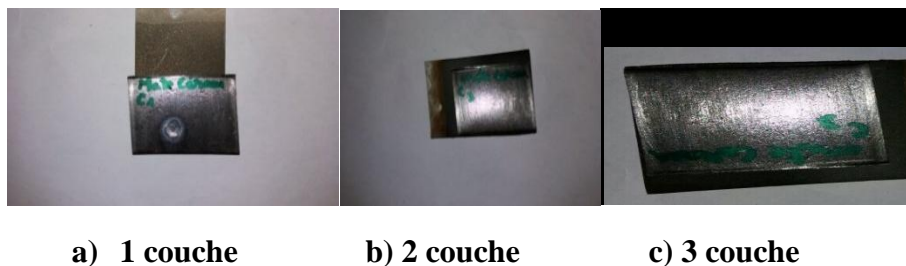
Soudage acier / aluminium / revêtement MetaCeram interposé.
